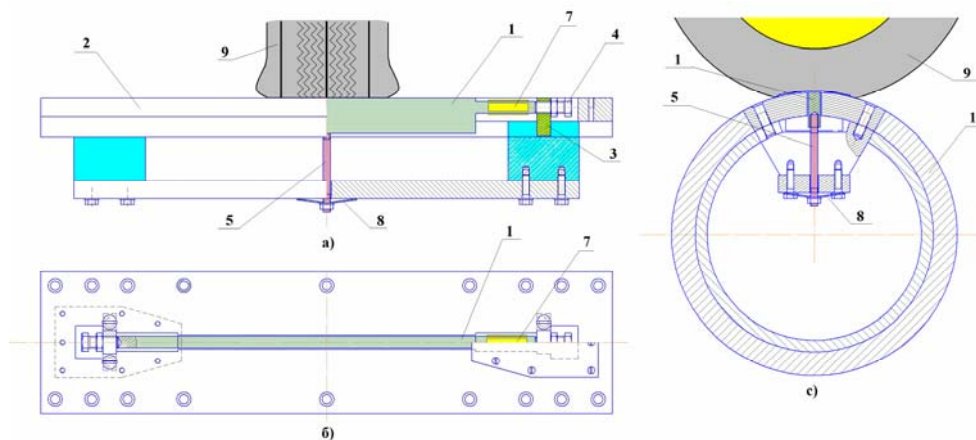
Датчик для измерения напряжений в контакте шин с опорной поверхностью бегового барабана:
